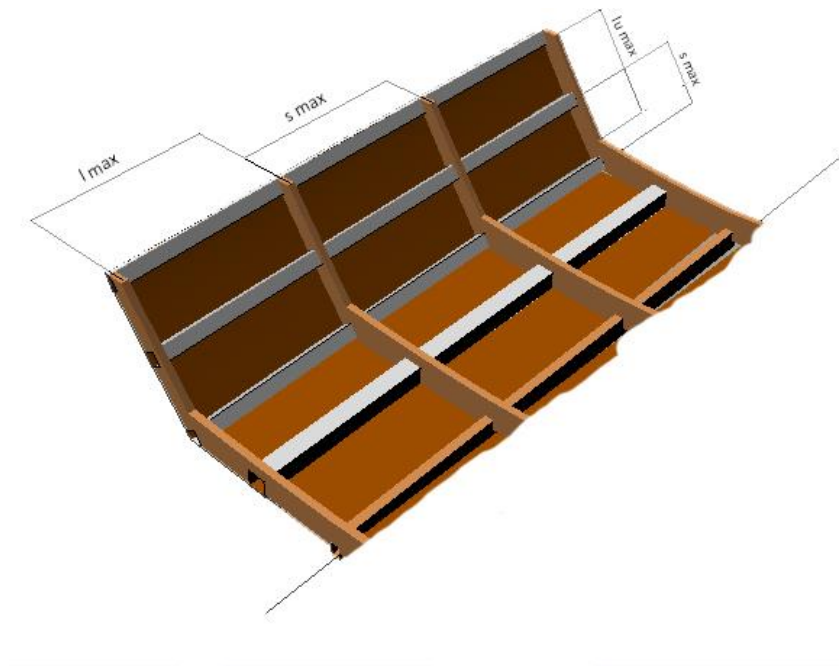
Imagen de la configuración de los refuerzos transversales y longitudinales
